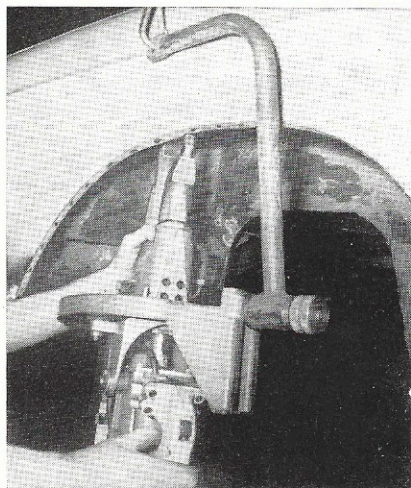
Soudage de la tôle formant panneau arrière sur traverse arrière supérieure. Pince ARO.
